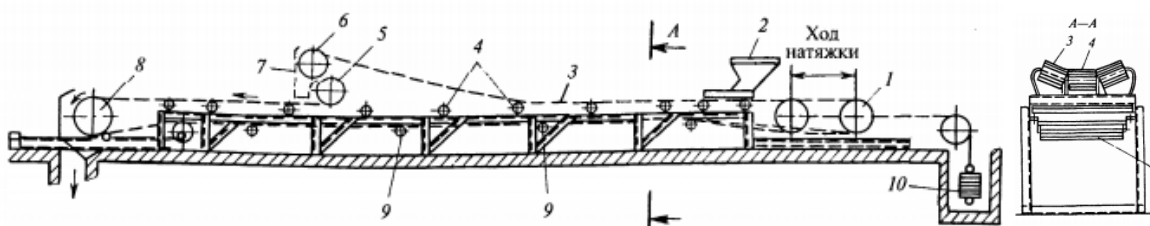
Ленточный питатель 1 — натяжной барабан; 2 — загрузочная воронка; 3 — лента; 4, 9 — опорные ролики; 5,6 — барабаны сбрасывателя; 7 — лоток; 8 — приводной барабан; 10 — груз для натяжения ленты
